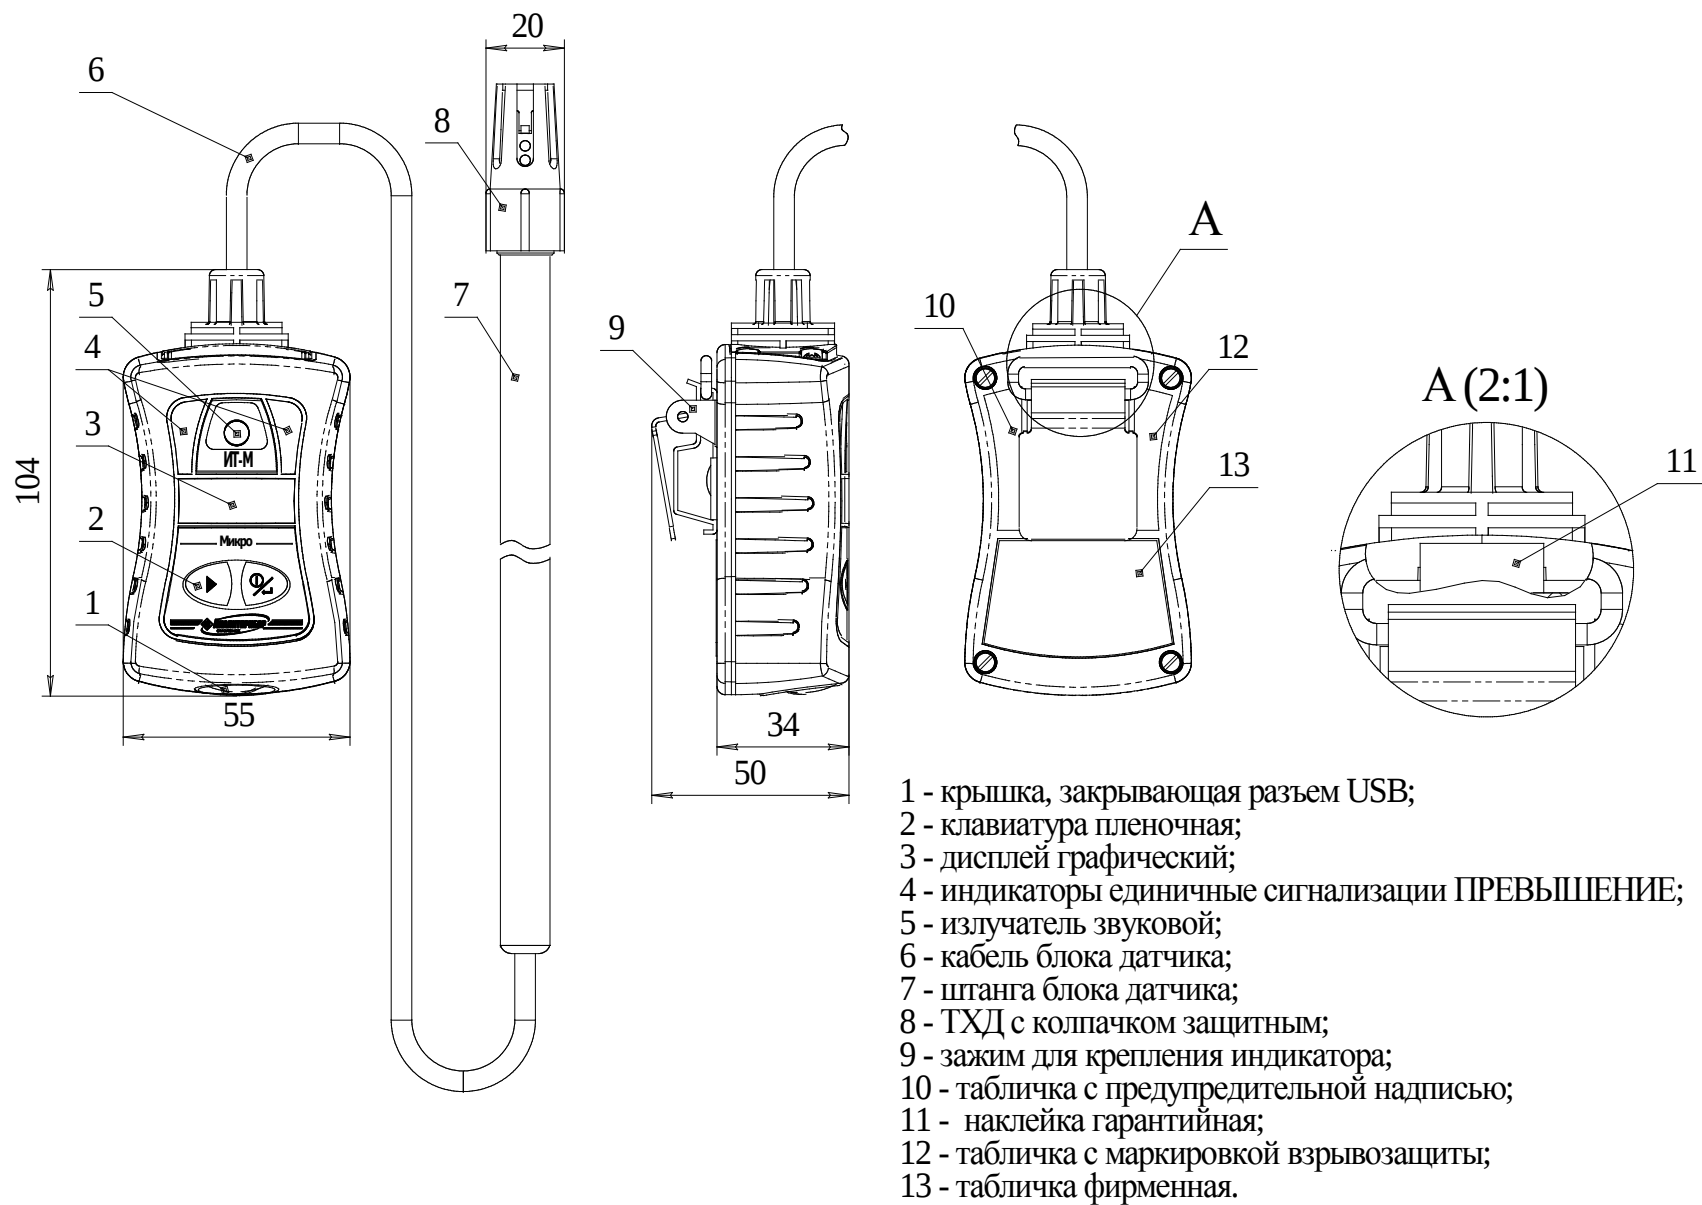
Индикатор-течеискатель горючих газов ИТ-М Микро. Внешний вид
